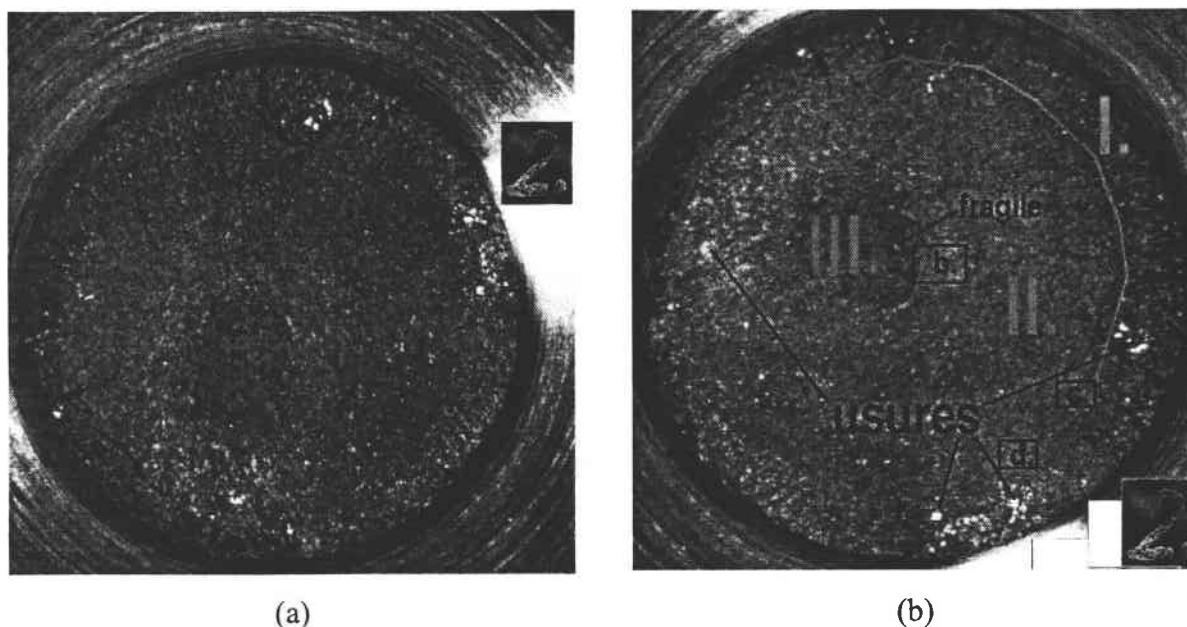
Aspect macrographique d'éprouvettes entaillées ($\rho = 0,4$ mm) soumises au chargement de flexion rotative : a) vue générale b) division de la surface.
